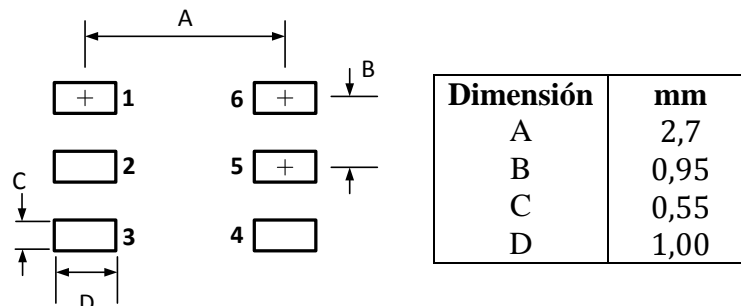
Dimensiones para el Gate Driver en el PCB
